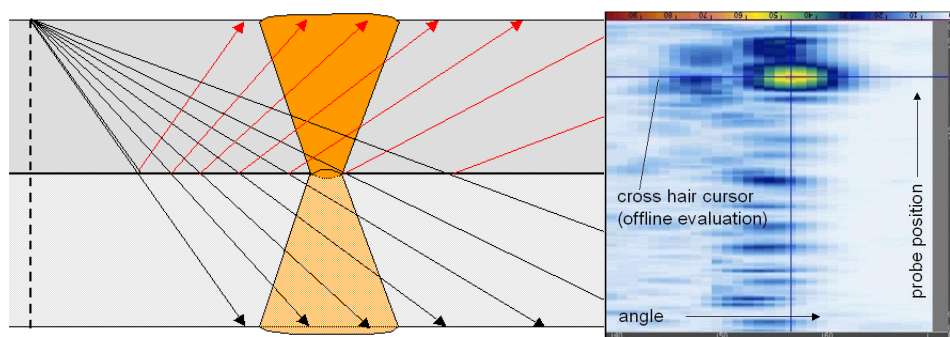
a) Escaneo de soldadura con reflejo montado para el escaneo C b) Vista superior de escaneo C ^[13]
